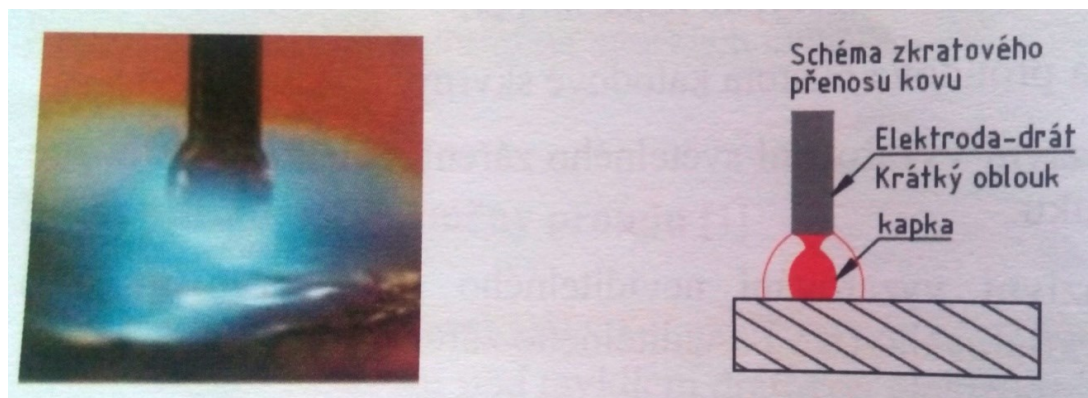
Princip svařování obalenou elektrodou v inertním plynu MIG [2]
